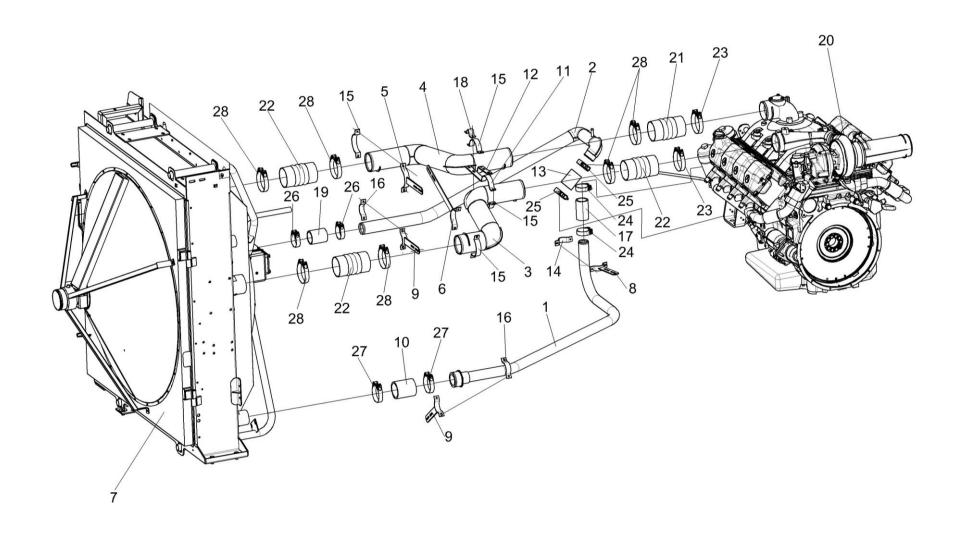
Установка двигателя OM502LA КВК 0150000 (установка блока радиаторов)
